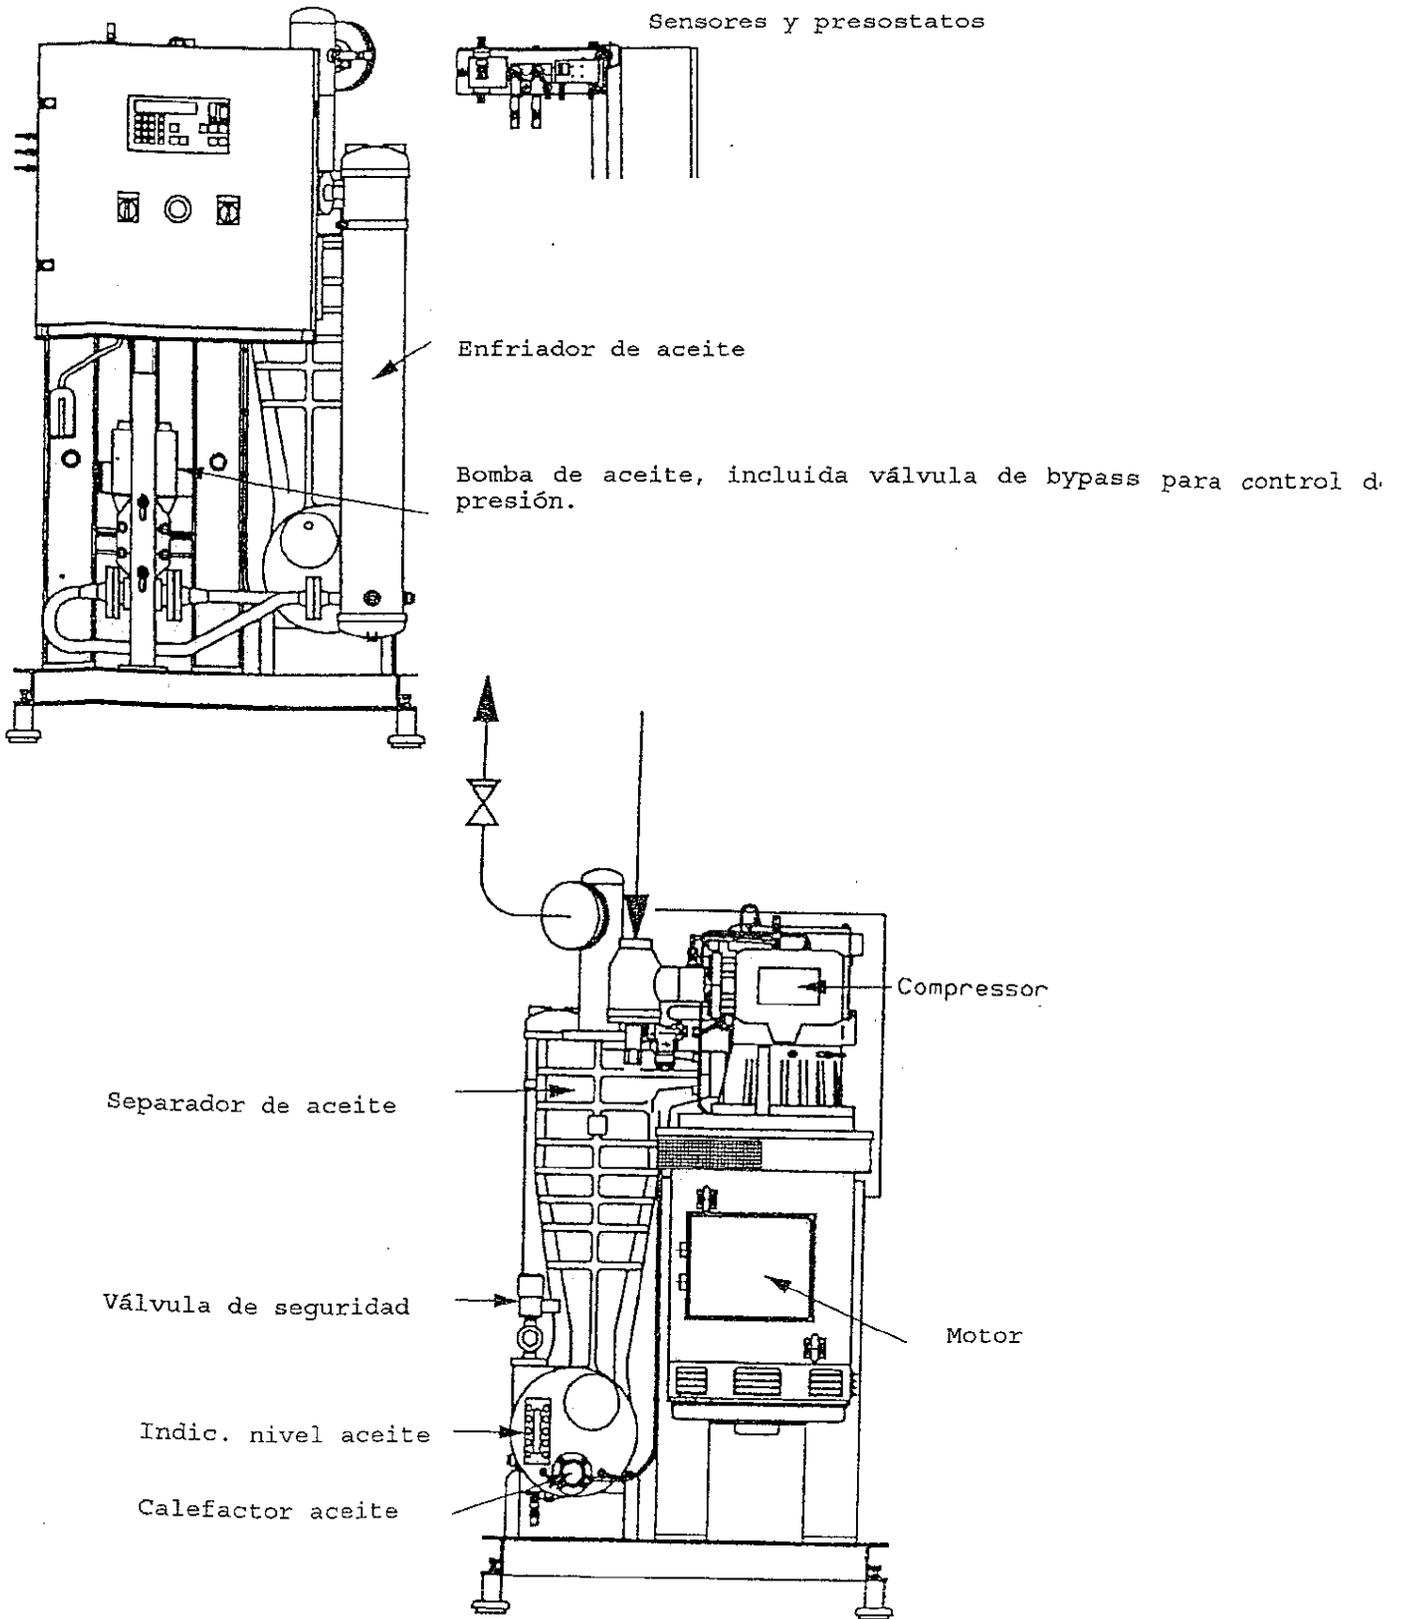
Unidad compresora Stal-Mini, componentes principales
